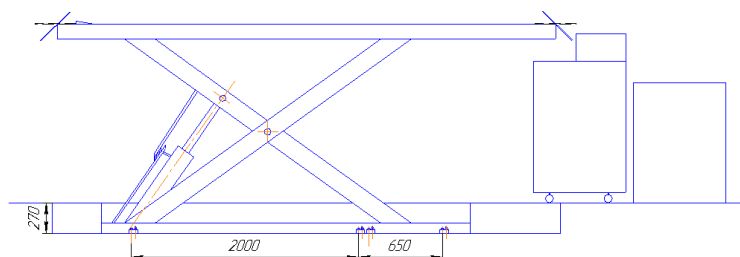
Фронтальный вид стенда на месте установки
